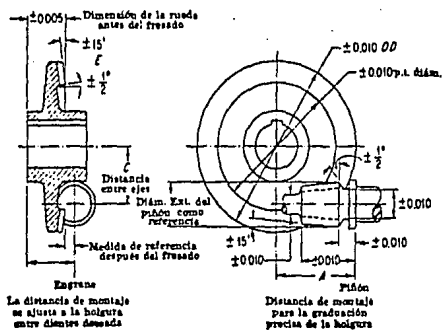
TOLERANCIAS PARA LOS ENGRANAJES ESPIROIDALES.
